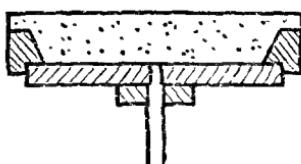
Гипсовый диск («болван»), вложенный в металлическое кольцо головки круга
